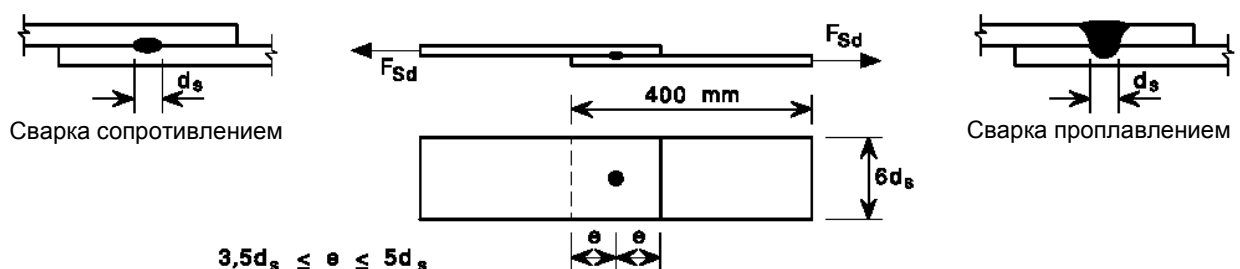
Образцы для испытаний на срез сварных точек
